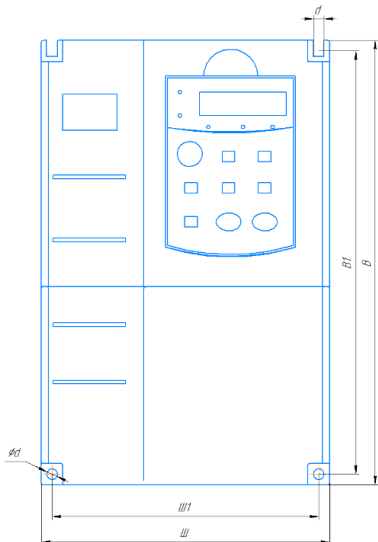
а - габаритные и установочные размеры устройств серии LCI в пластмассовом корпусе
